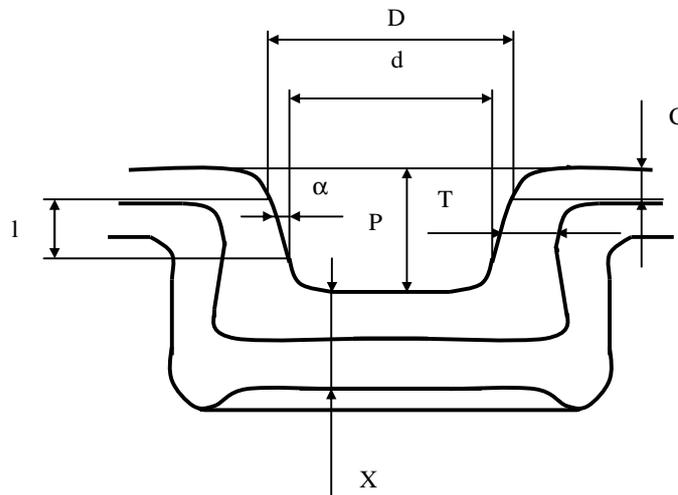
Dimensiones más importantes que se pueden apreciar en una unión de botón.
